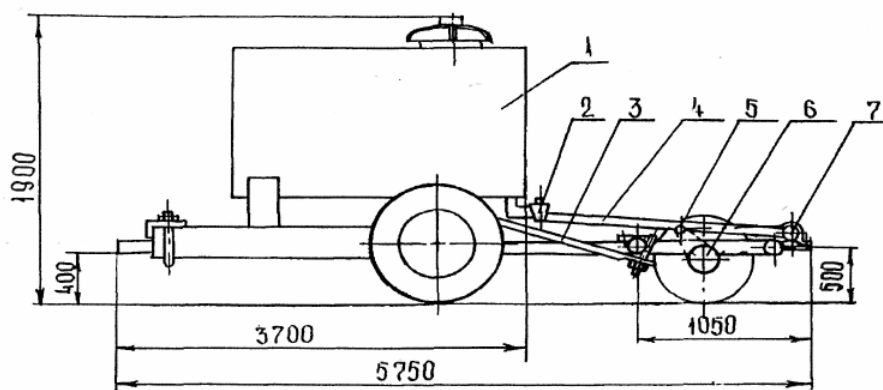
Общий вид агрегата (вид сбоку):
